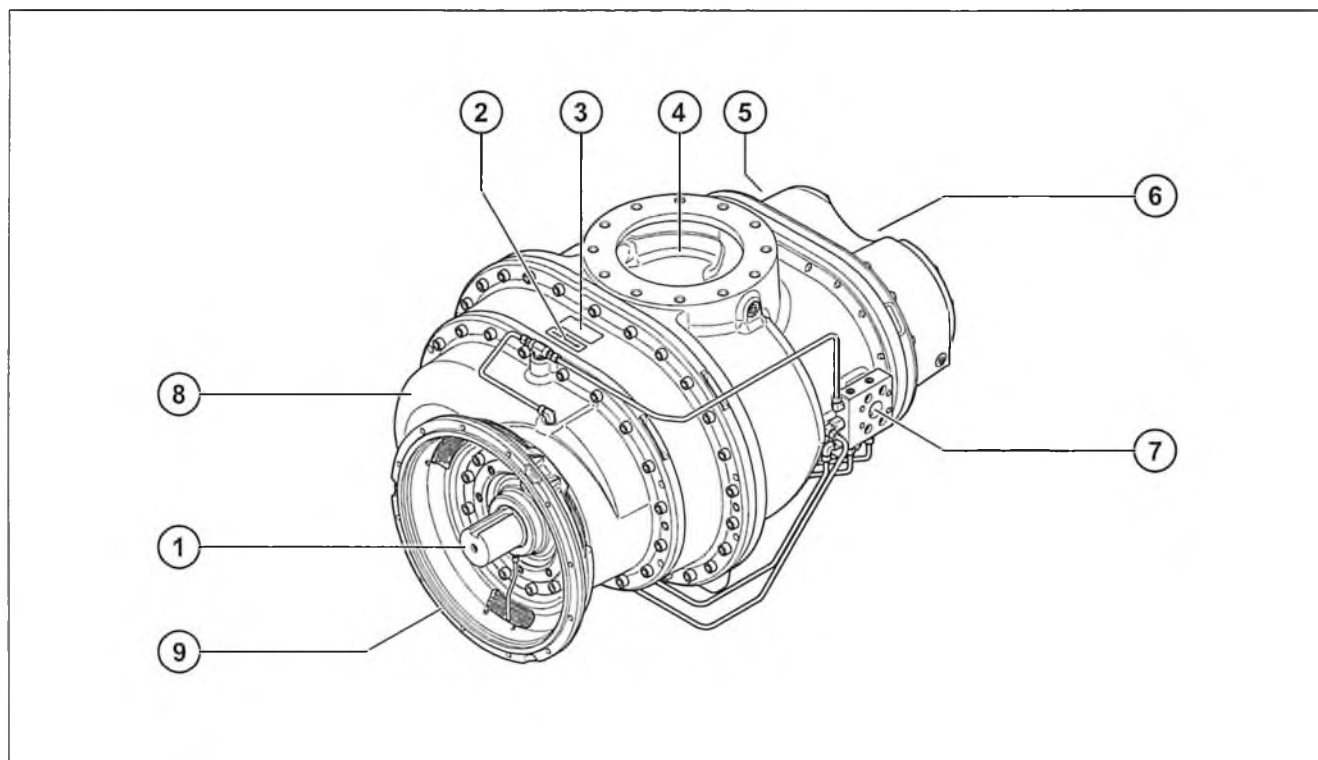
Газовый винтовой компрессорный блок EVO-G-Gas (с редуктором, пример)
